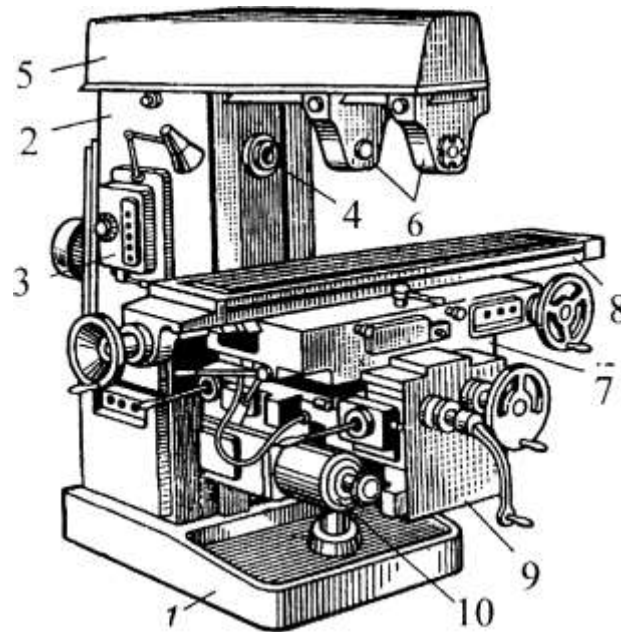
Устройство горизонтально-фрезерного консольного станка
